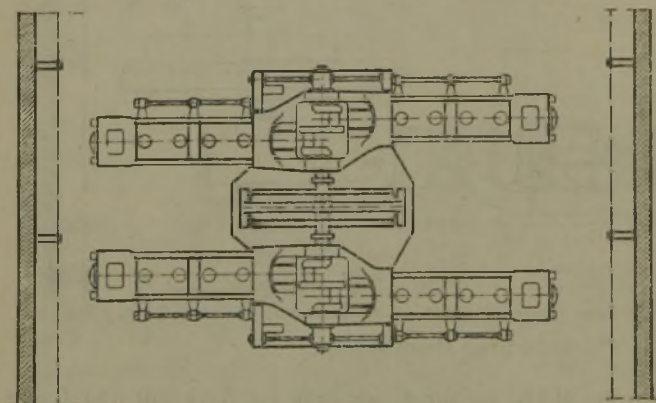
MAN.-Großgasmaschine für 5000 PS, neueste Bauart.
